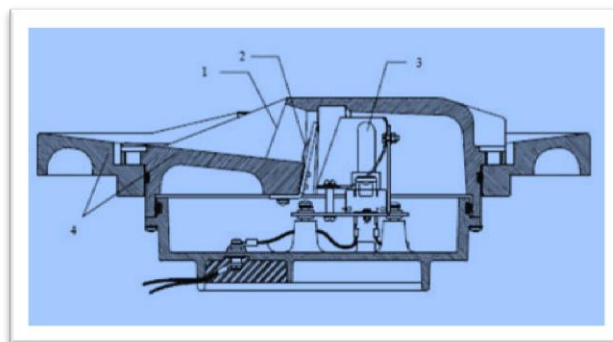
Luminaria empotrada montada en base metálica y aro adaptador
